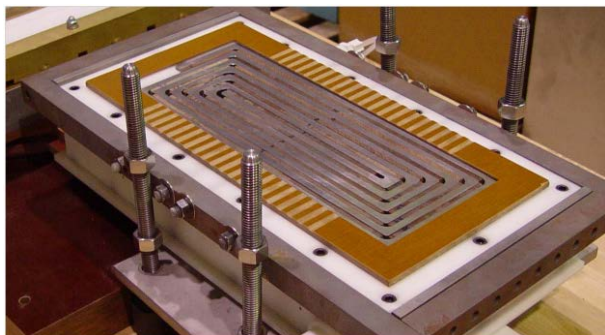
Atuador plano para moldar chapas metálicas[36].
